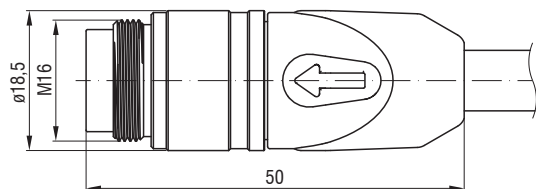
Maßzeichnung Stecker Sensorkabel
